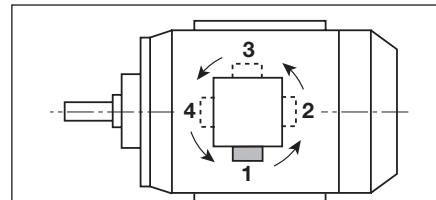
U - Verlauf der Kabeleinführung auf dem Grundriss
